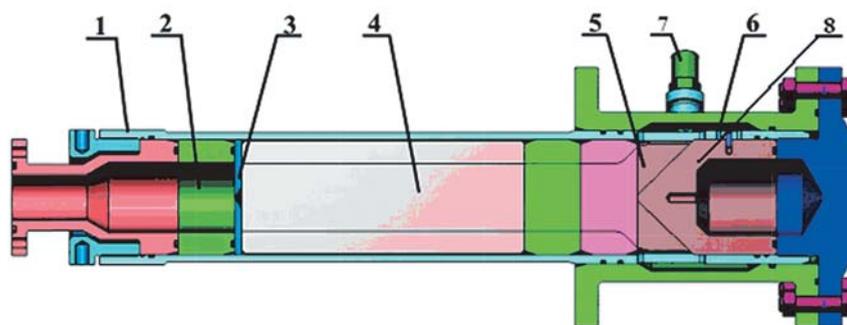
Конструктивная схема экспериментального излучателя колебаний: 1 – корпус излучателя; 2 – предсопловая камера; 3 – сопло; 4 – камера; 5 – выходные каналы; 6 – коллектор; 7 – выходное сопло; 8 – разделитель потока.
